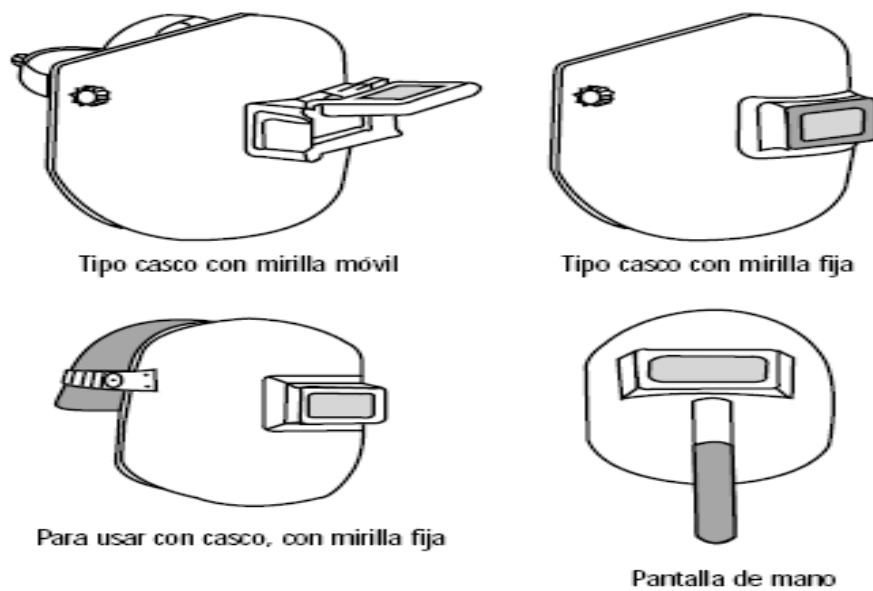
Protectores para trabajos de soldadura.
